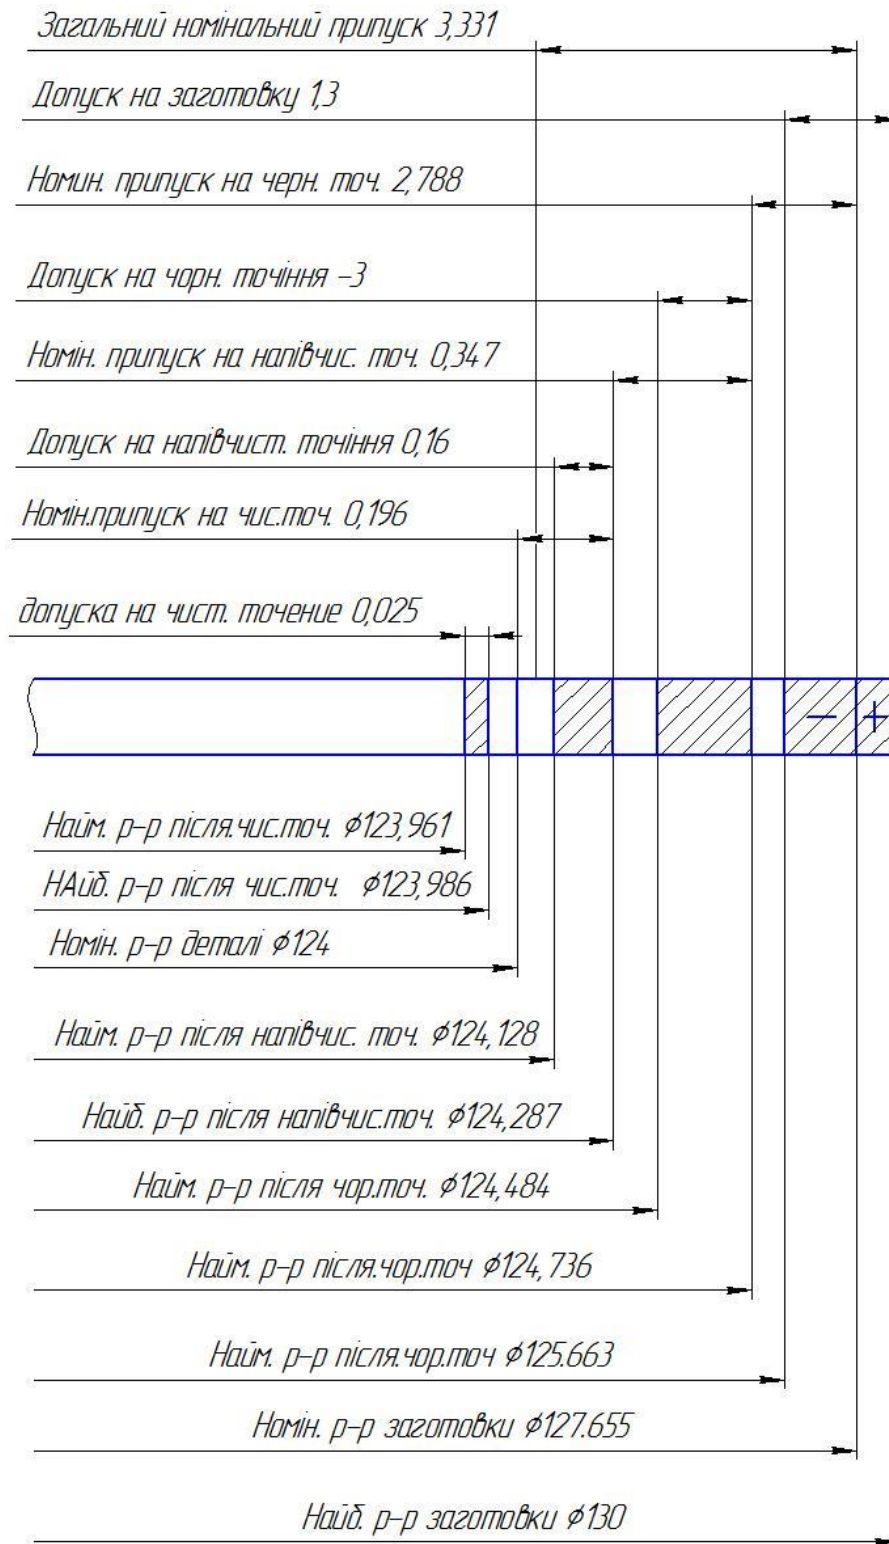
Схема розташування допусків і припусків на оброблення поверхні  $\phi 124_{-16}$  заготовки ролика
